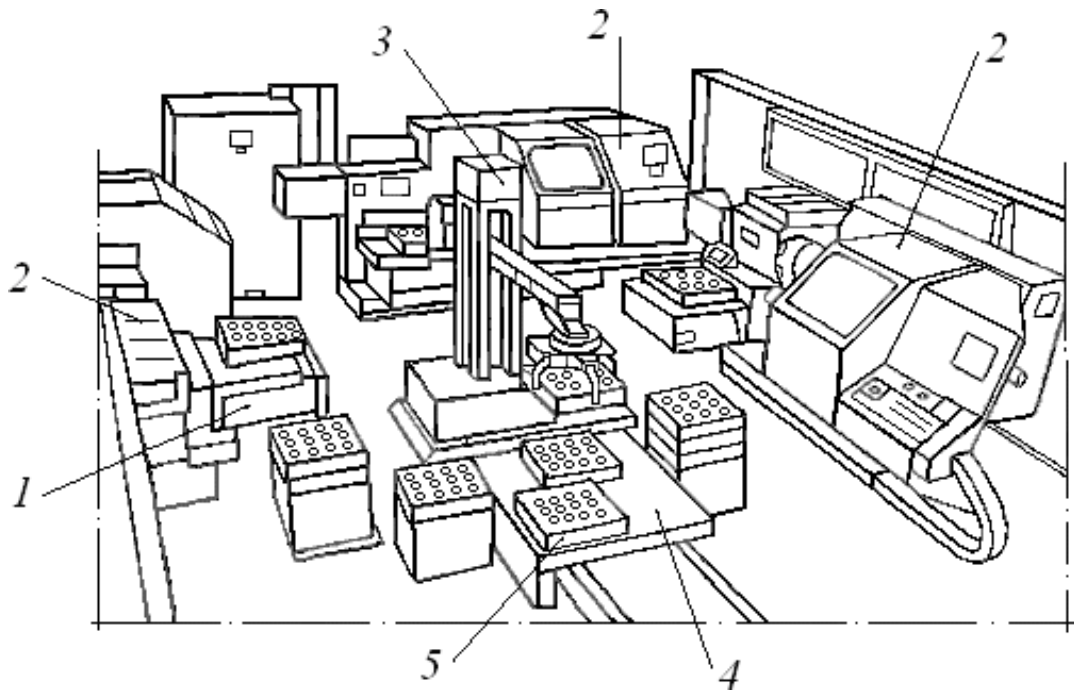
Компонівка гнучкого виробничого комплексу механообробки тіл обертання
